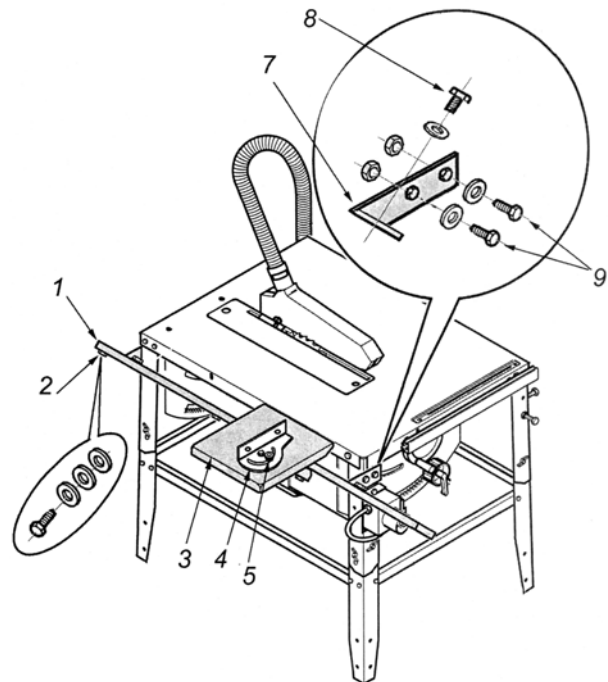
Montaje del carril de rodadura y el carro deslizante
